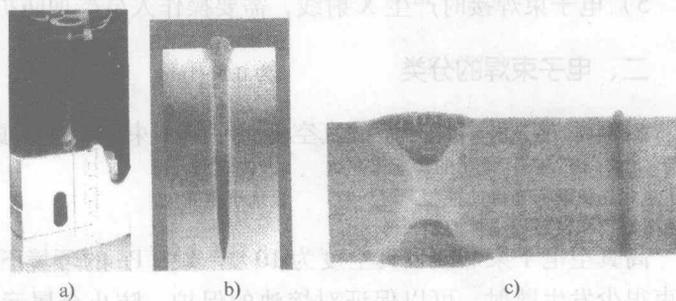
电子束焊接过程示意图及焊缝的特征
